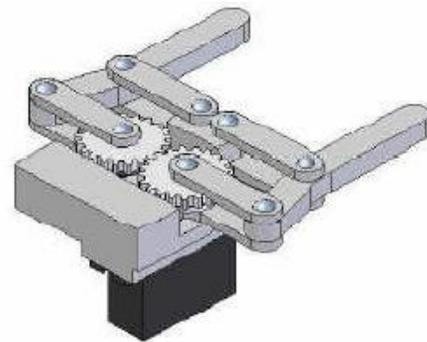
Pinza (fuente: sistema mecatrónico para la selección de ejes y engranajes)
